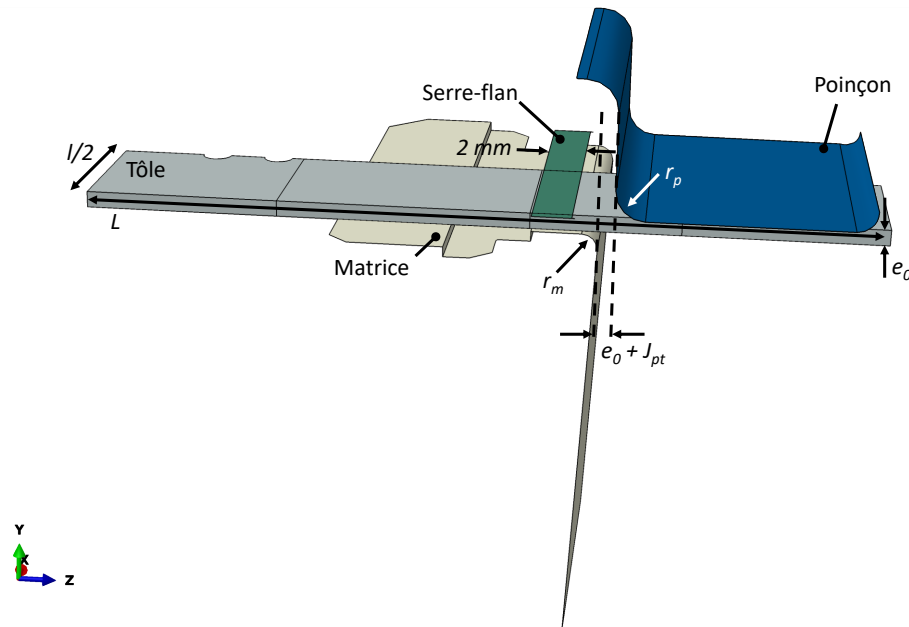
Modèle numérique de cambrage illustré pour une géométrie d'éprouvette de longueur L et de largeur l et géométries des outils
